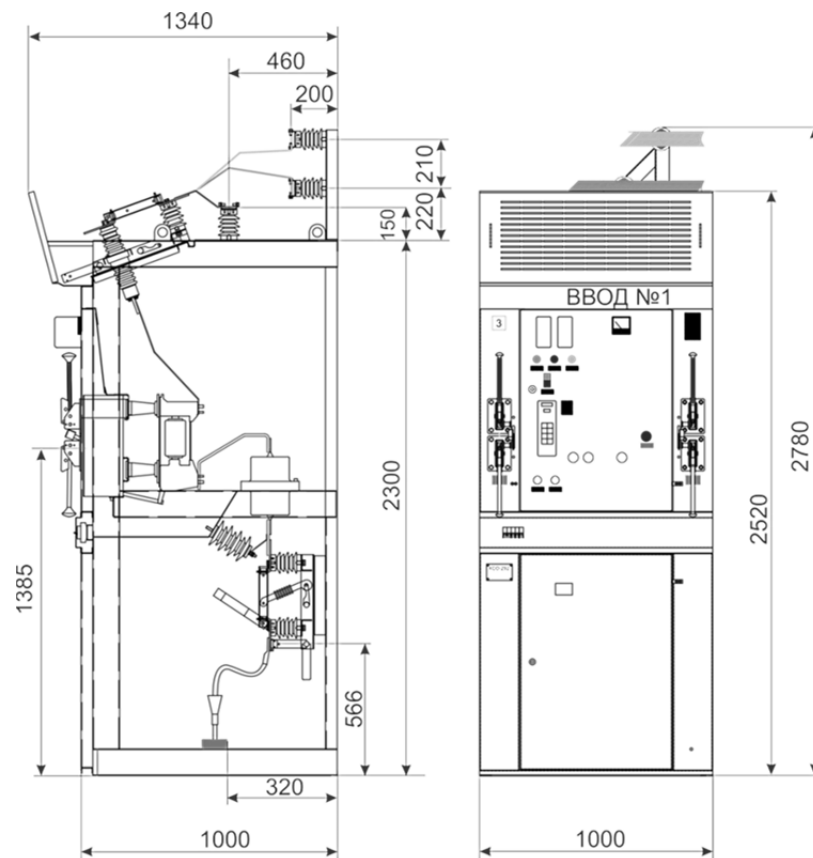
Габаритные размеры камеры КСО-292-КЕМ/kz
